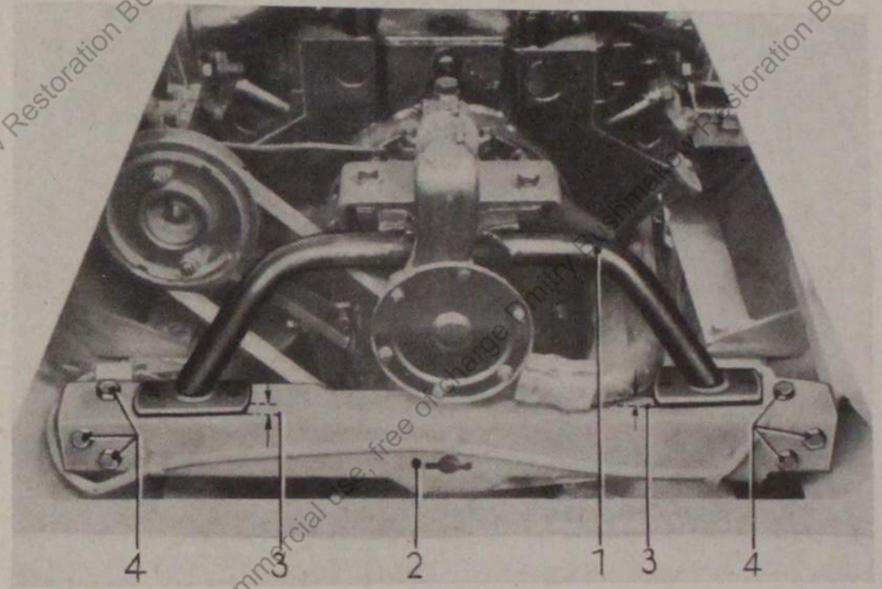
Motorträger vom hinteren Rahmenquerträger abgehoben
